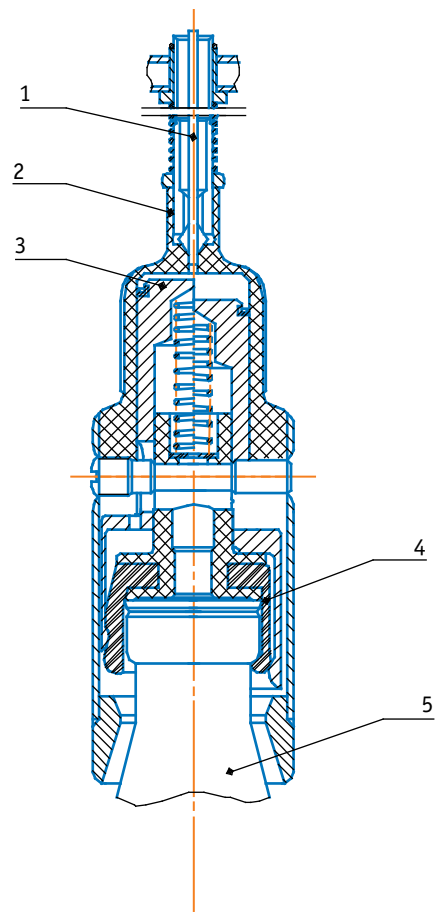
Пневмопатрон: 1 — патрубок подачі стисненого повітря; 2 — корпус; 3 — поршень; 4 — еластична манжета; 5 — пляшка
